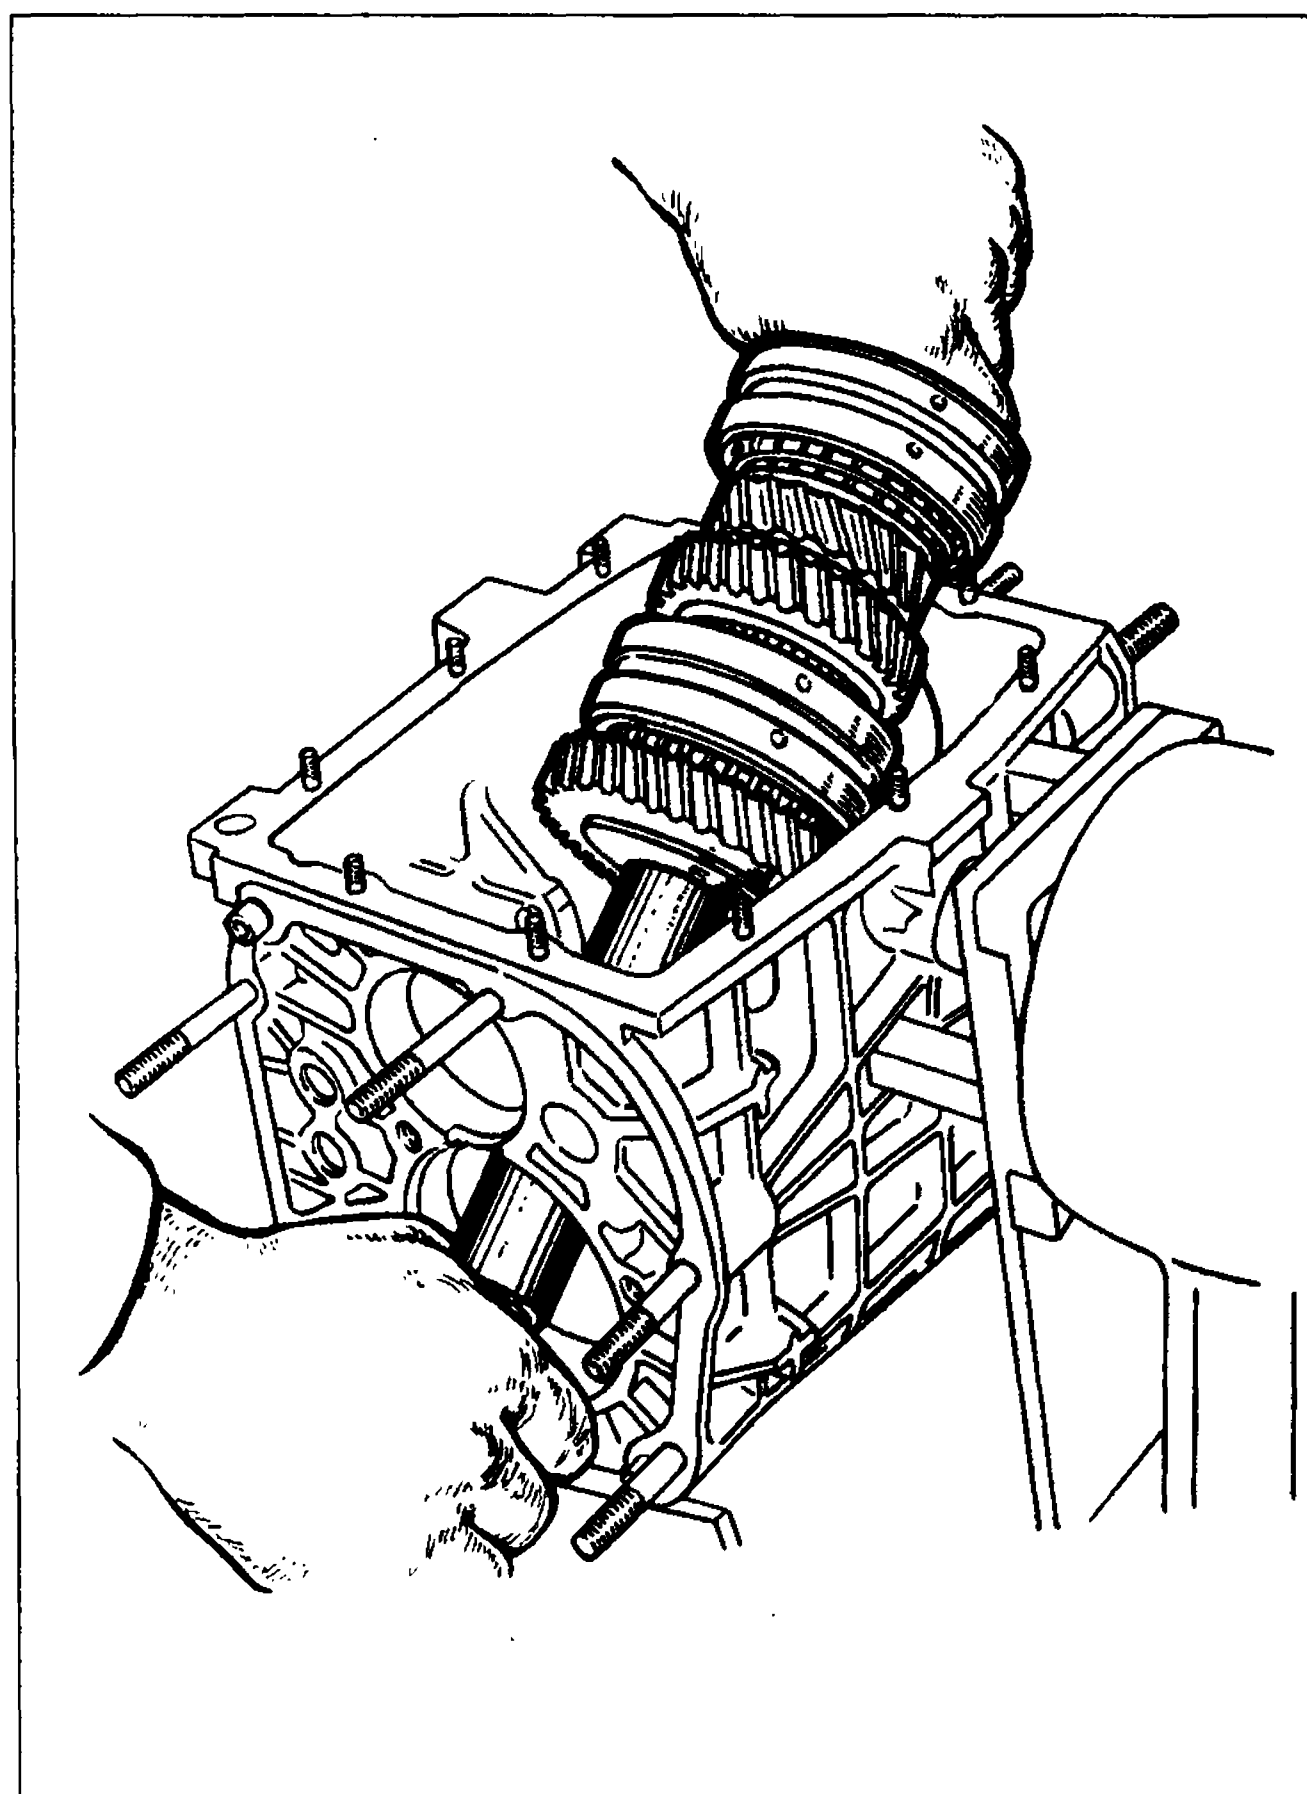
Извлечение вторичного вала из картера коробки передач
